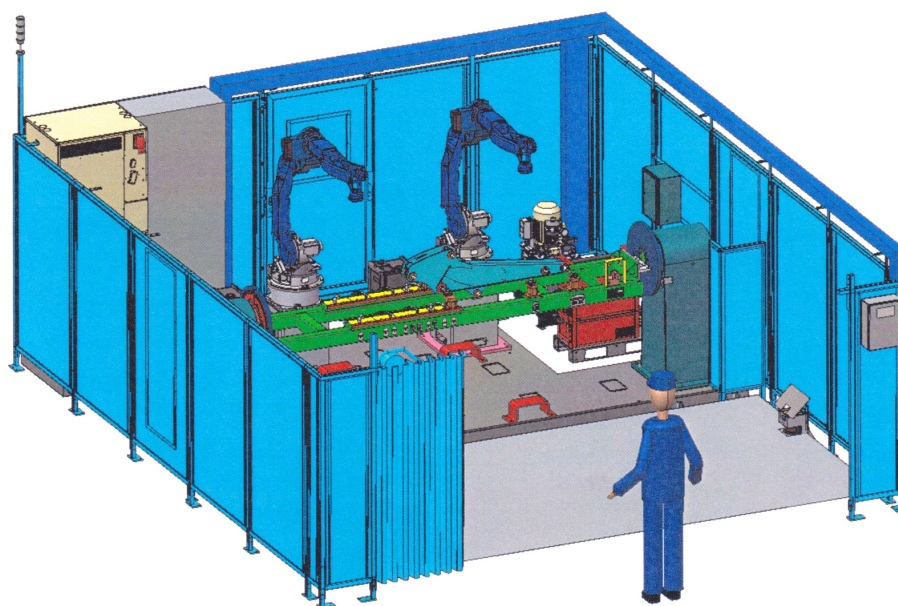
Výložník založen do přípravku pro robotické svařování – boční pohled
